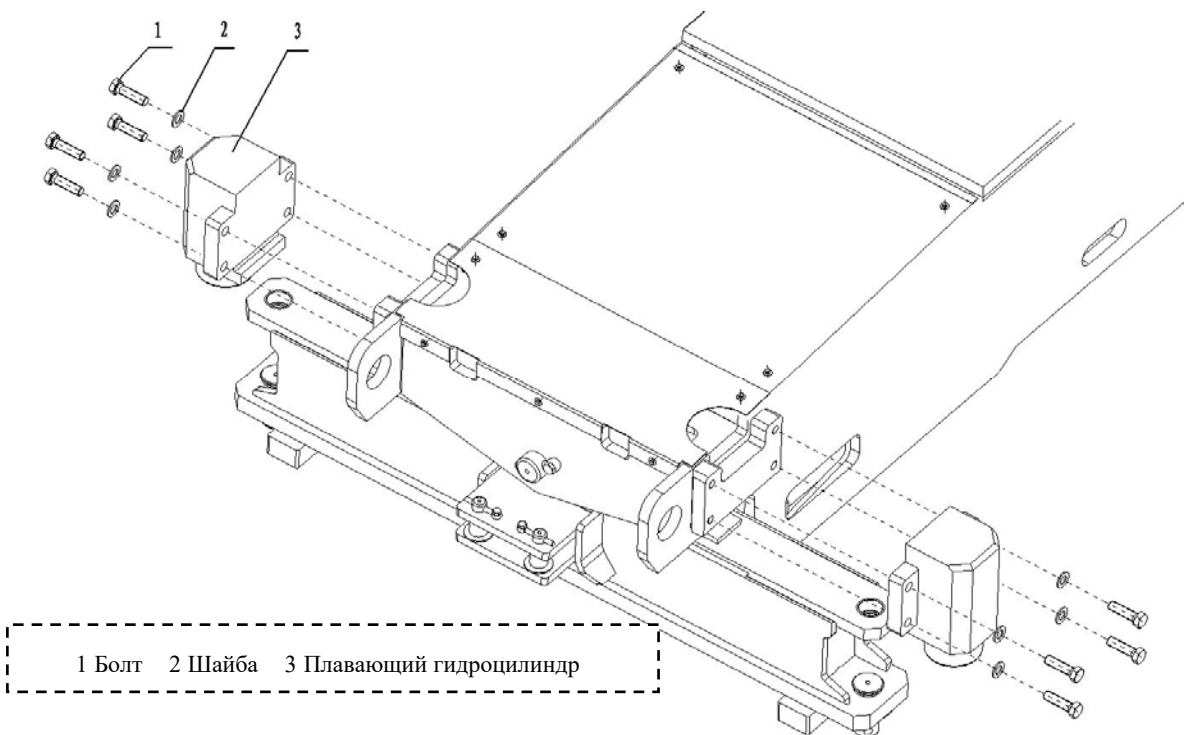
Схема разборки плавающего гидроцилиндра
